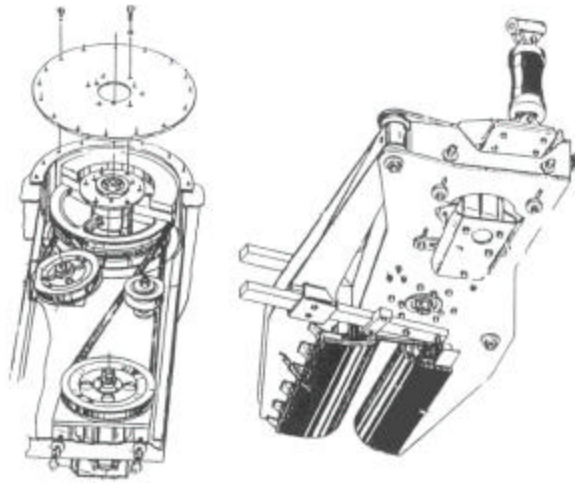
Cabeza vibradora. Sistema de accionamiento de las masas y vista inferior (doc. Halcón).
